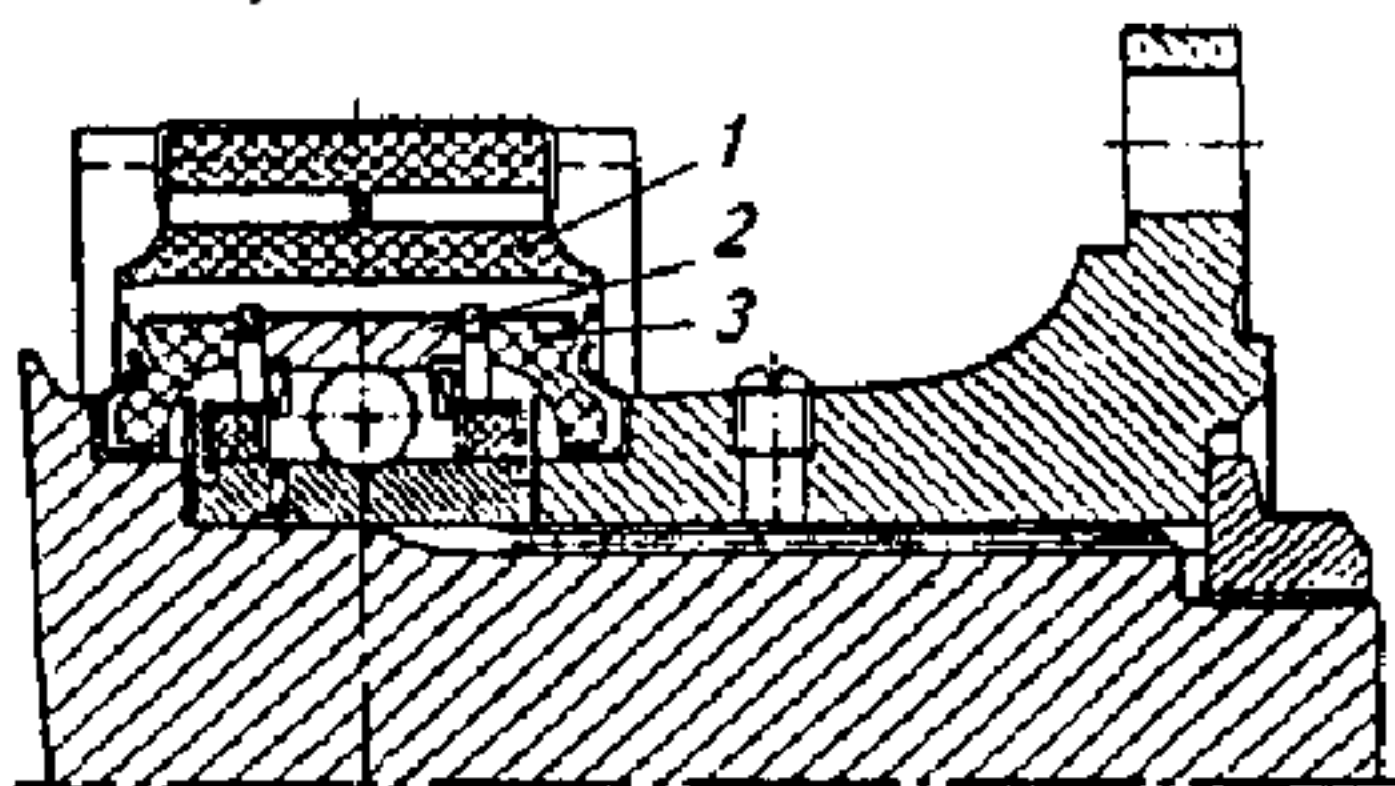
Промежуточная опора карданной передачи: 1 — упругий элемент; 2 — опорный шарикоподшипник; 3 — защитное уплотнение
